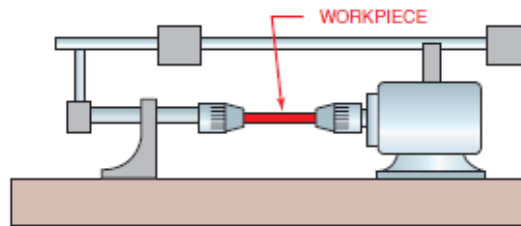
Máquina de ensayo de tracción para medir la resistencia de soldaduras (máquina de prueba de 60,000 Lb)
